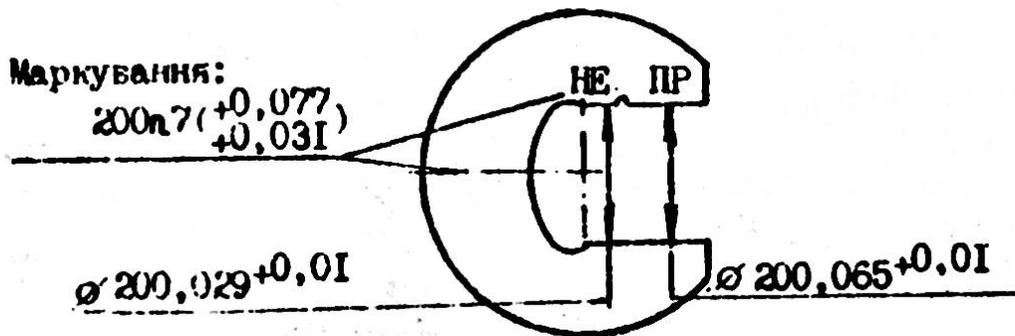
Калібр-скоба для контролю вала Ø200 n7
